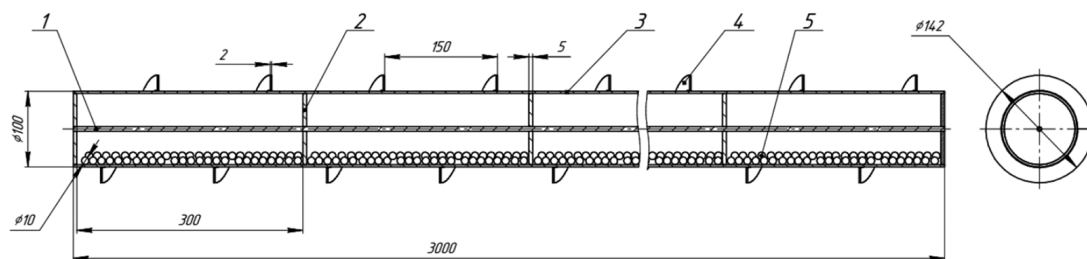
Продольный разрез шнека: 1 – ось; 2 – перегородка; 3 – труба; 4 – спираль; 5 – шарик
